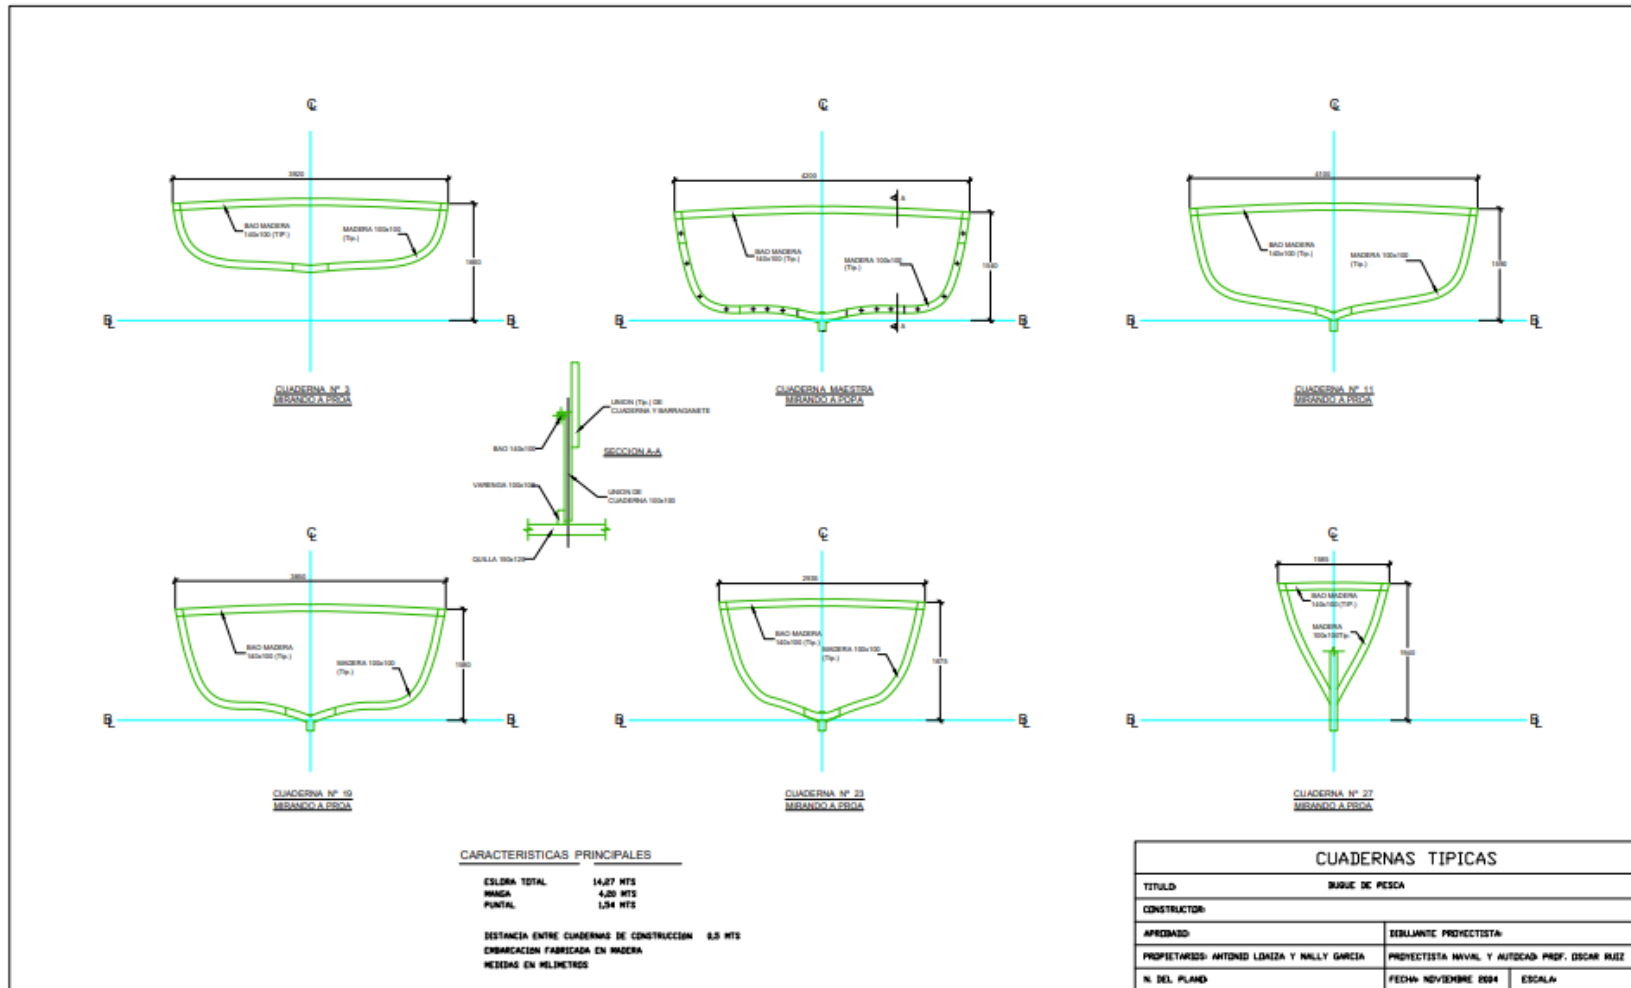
Planos cuadernas de la nave menor fuente: Bilocad
